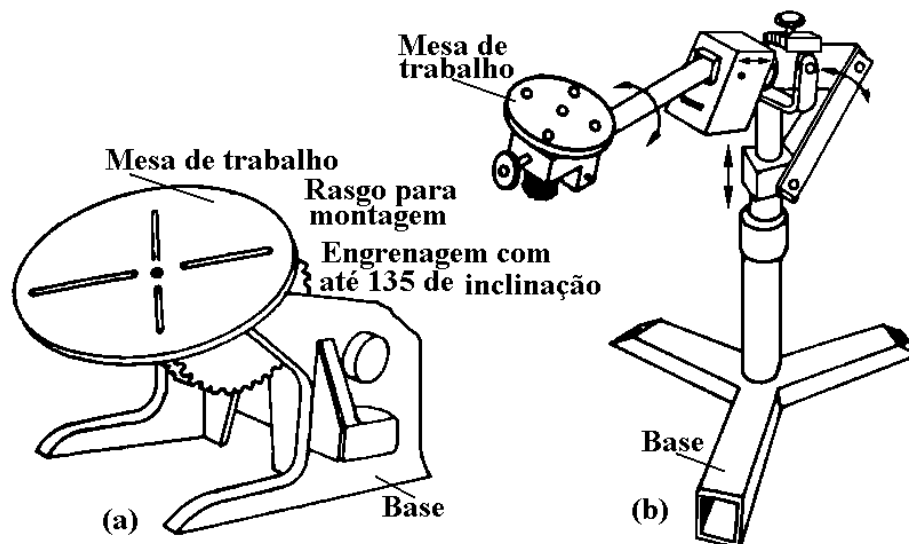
Mesa e balança posicionadoras, (a) Mesa posicionadora com engrenagem motora, (b) Balança posicionadora
